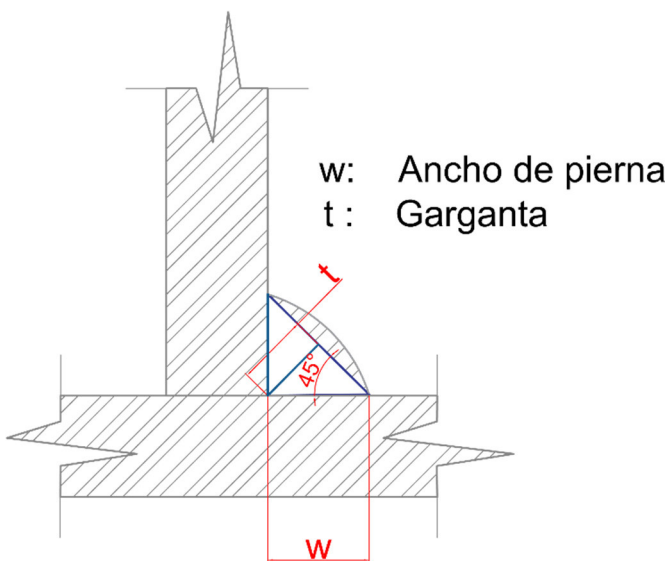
REPRESENTACIÓN DE LA GARGANTA Y ANCHO DE PIERNA EN CORDÓN DE SOLDADURA TIPO FILETE EN T
